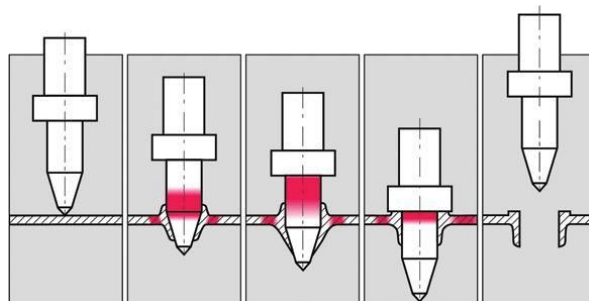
Стадии процесса формообразования отверстия пластическим сверлением
